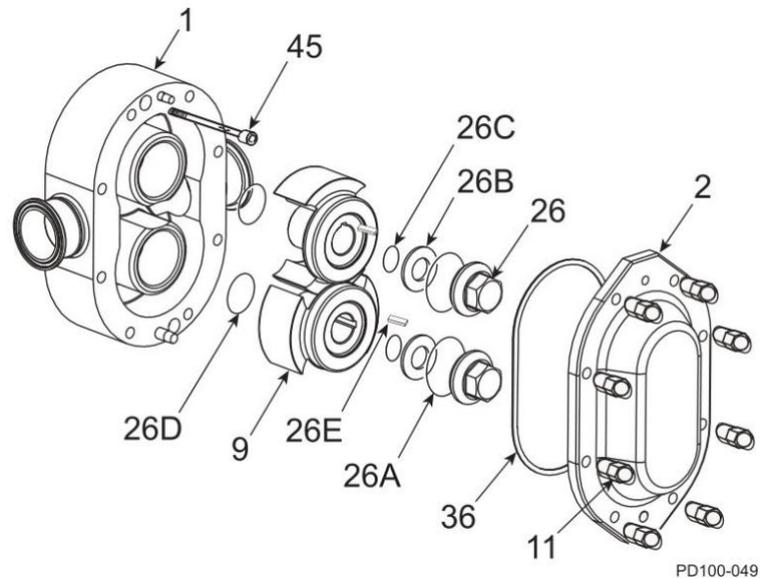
Explosionszeichnung des Fluidkopfes
